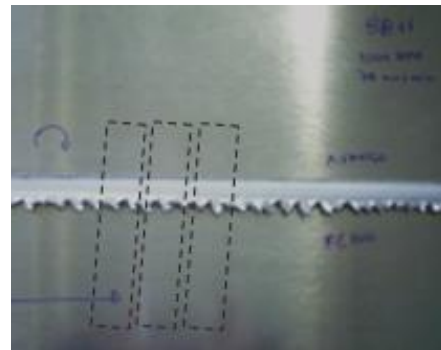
Provette obtido após a soldadura de FSW.
